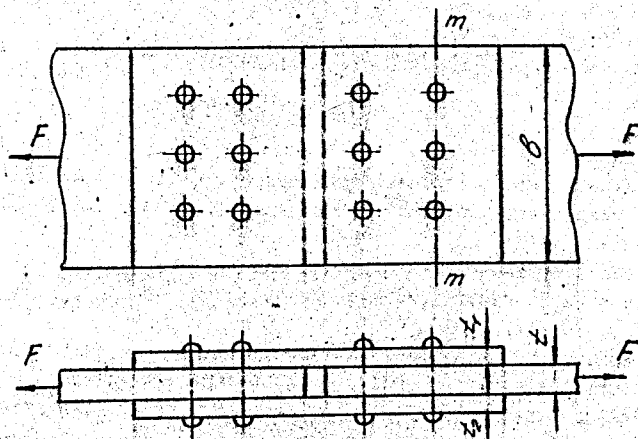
Схема до розрахунку заклепочного з'єднання
